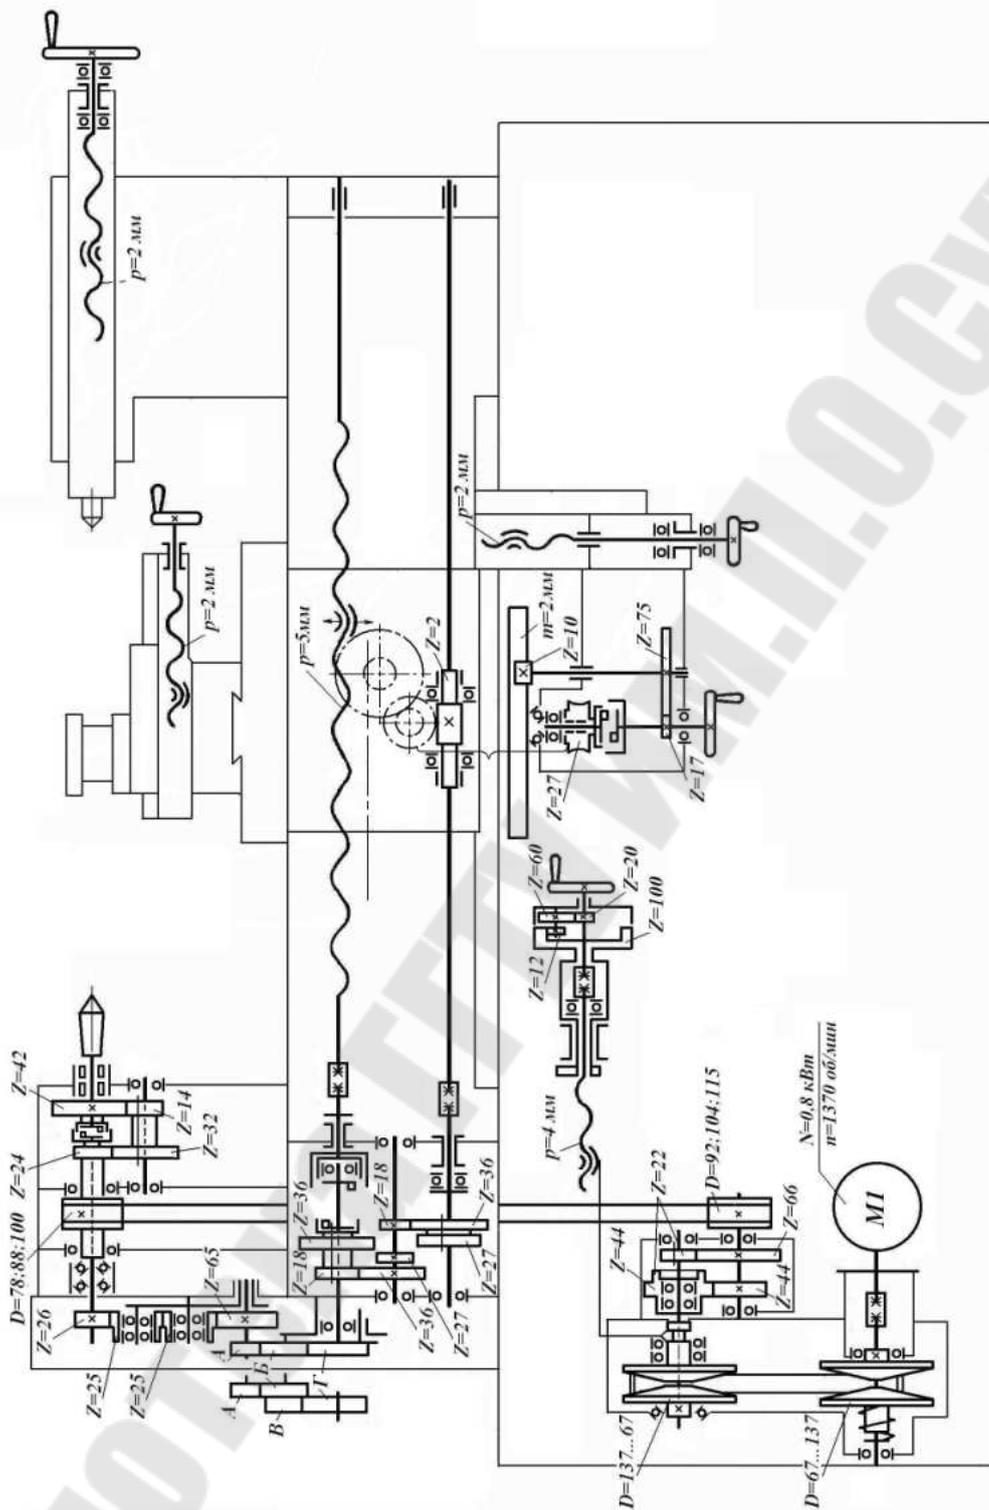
Кинематическая схема токарного станка 16У03П
